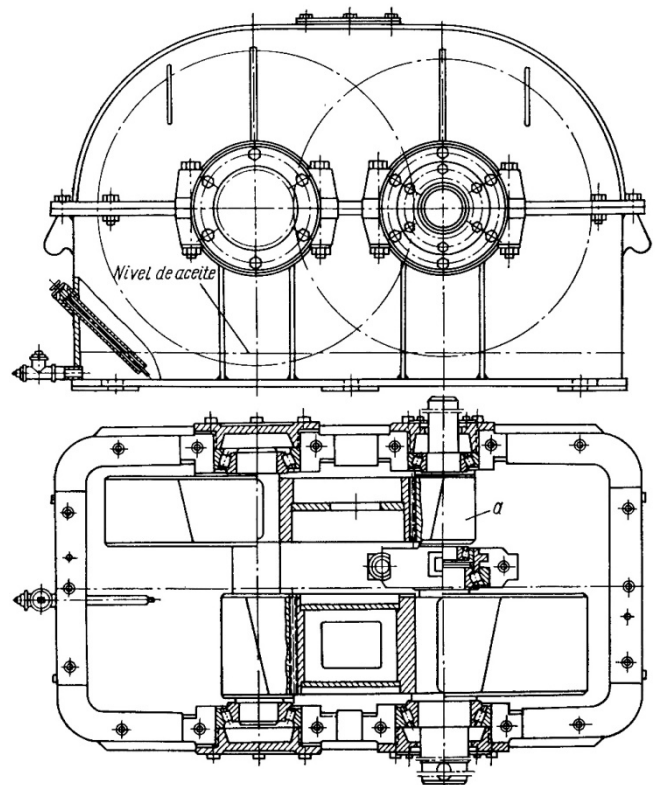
Reductor de engranajes cilíndricos de 2 etapas, concurrente. (Ref.1)
